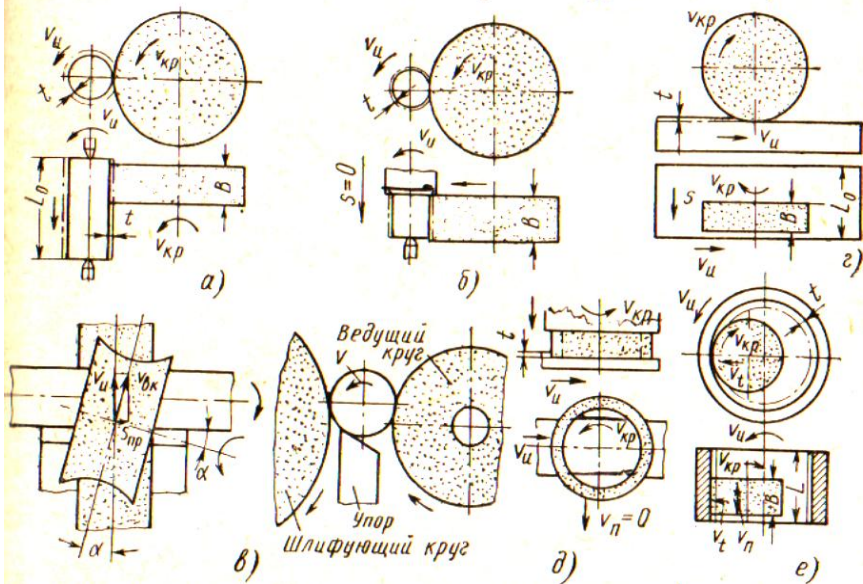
Схемы резания при шлифовании: а-наружное с продольной подачей; б- наружное с поперечной подачей; в-бесцентровое; г – плоско периферией круга; д – торцом круга; е – круглое внутреннее
